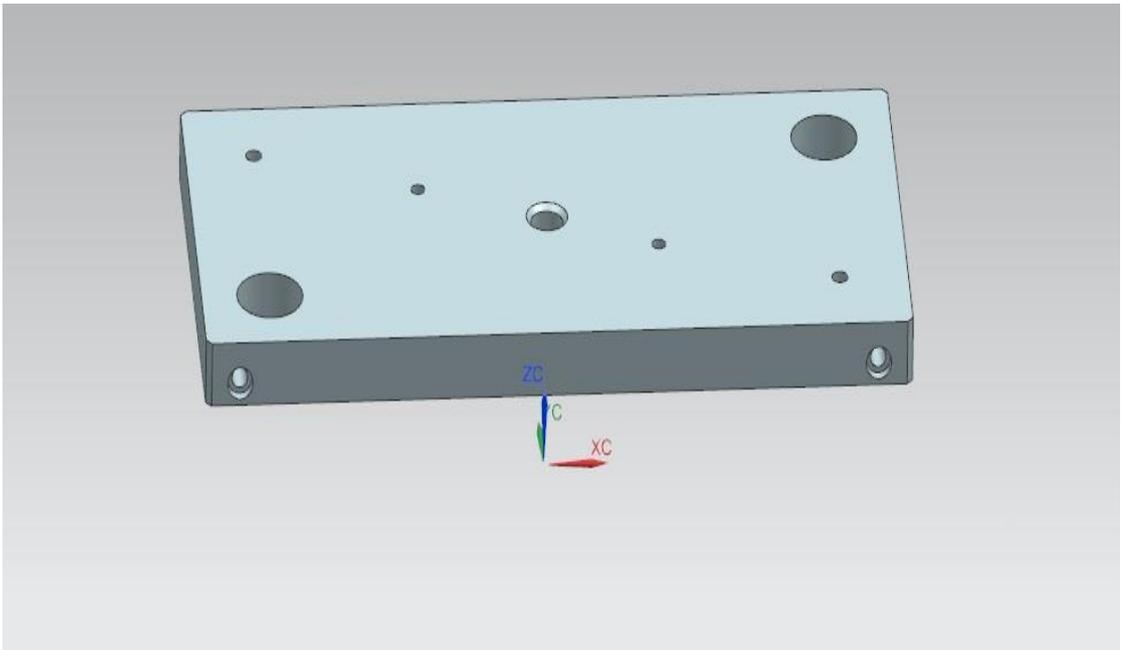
Верхняя плита для прессы K2028 – 0.63 МН
